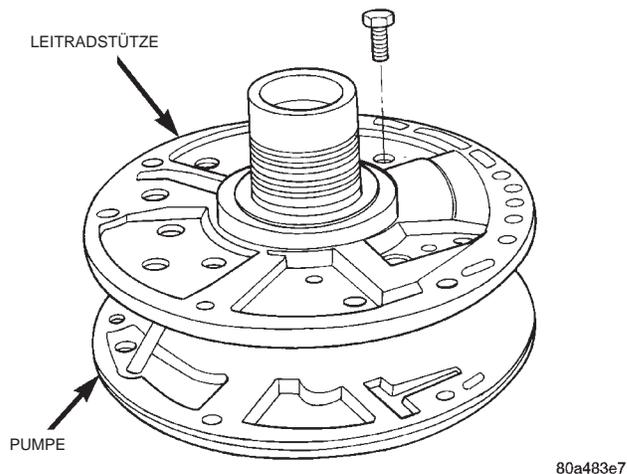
Schrauben Pumpengehäuse/Stütze herausdrehen
